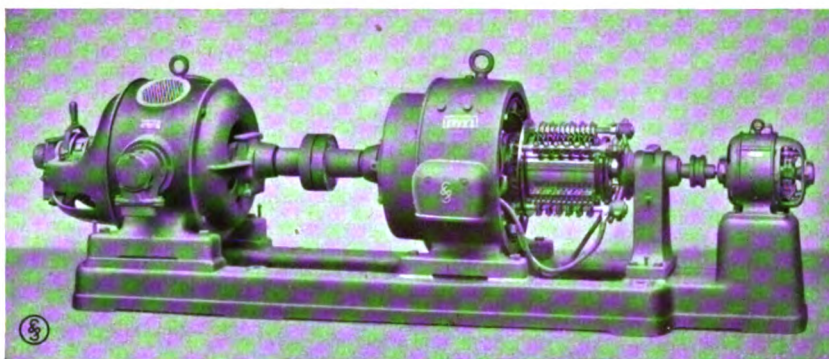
Ortsfeste Schweißanlage für 500 A Dauerstrom.
